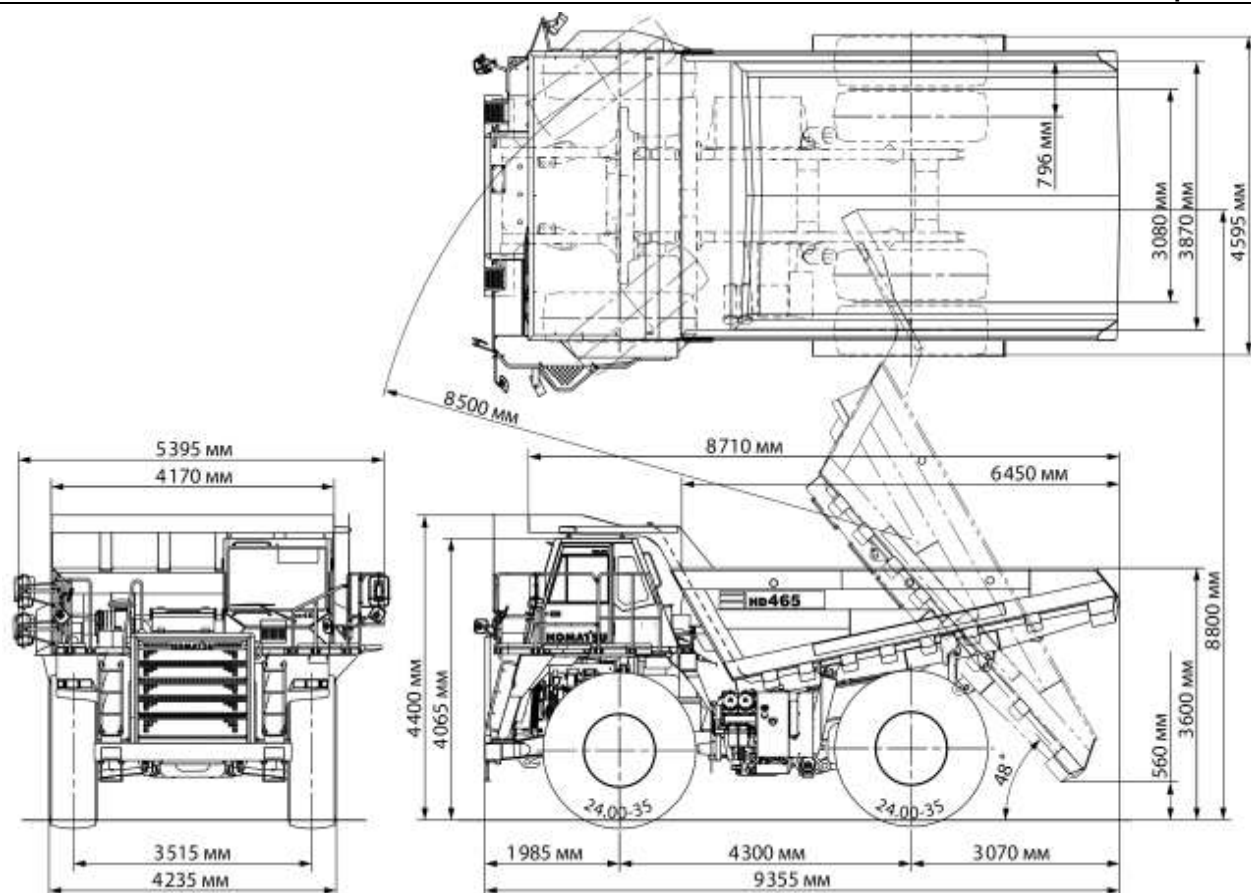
Габаритные размеры автосамосвала Komatsu HD465
